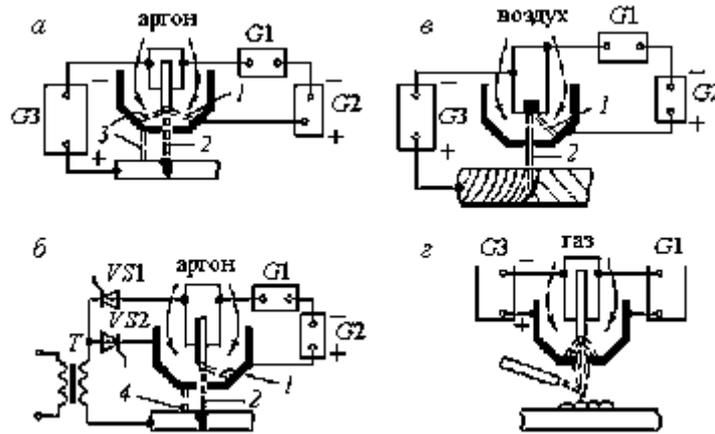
Схемы плазменных процессов: а- сварки на постоянном токе; б- сварки на переменном токе; в- резки; г- напыления
